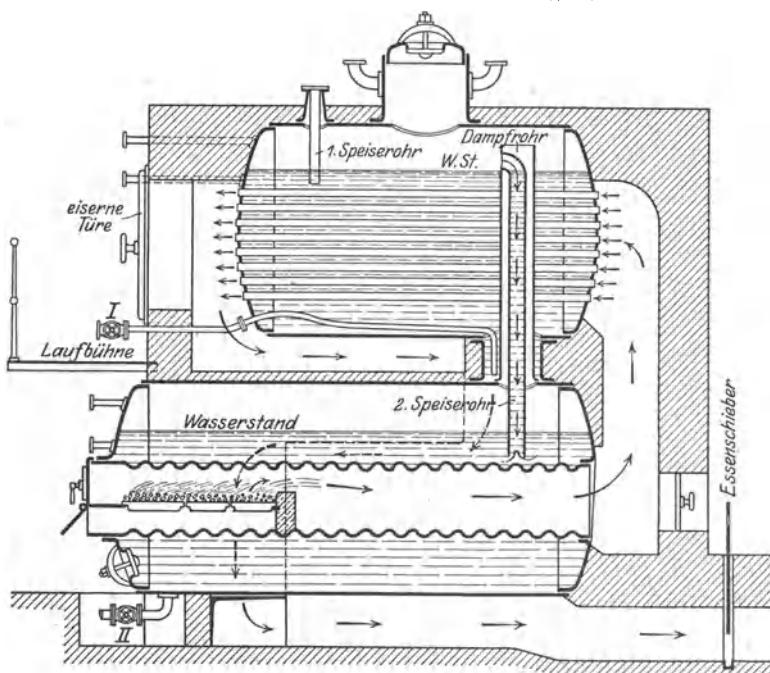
Kombinierter Kessel. Oben: Heizrohrkessel, unten: Zweiflammrohrkessel, beide mit je einem Dampfraum. Iu. II sind die Abläfventile. Gewöhnlich wird in den Oberkessel gespeist. Ist dieser genügend mit Wasser gefüllt, so läuft das hinzugespeiste Wasser durch das 2. Speiserohr (Überlaufrohr) in den Unterkessel. Letzterer hat außerdem für den Notfall eine besondere (nicht gezeichnete) Speiseleitung.
